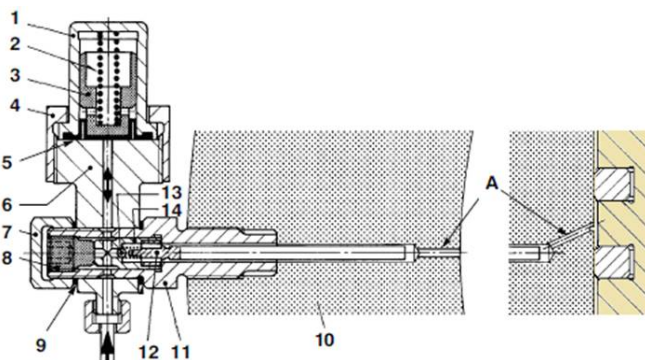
Складові лубрикаторної системи двигунів РТА: 1-кришка акумулятора; 2-пружина; 3-поршень; 4-накидна гайка; 5-мембрана; 6-корпус акумулятора; 7-гайка штуцера; 8-заглушка; 9-прокладка; 10-циліндрова втулка; 11-корпус штуцера; 12-стрижень; 13-кульковий клапан; 14-пружина клапана.
